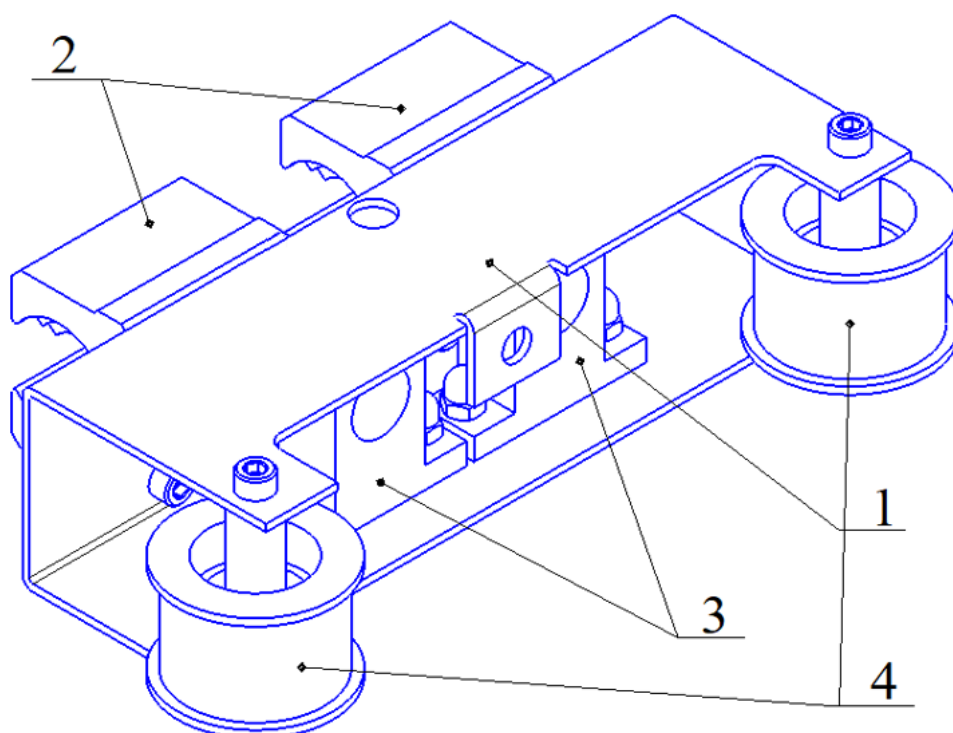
Корпус координатной платформы системы манипулирования
